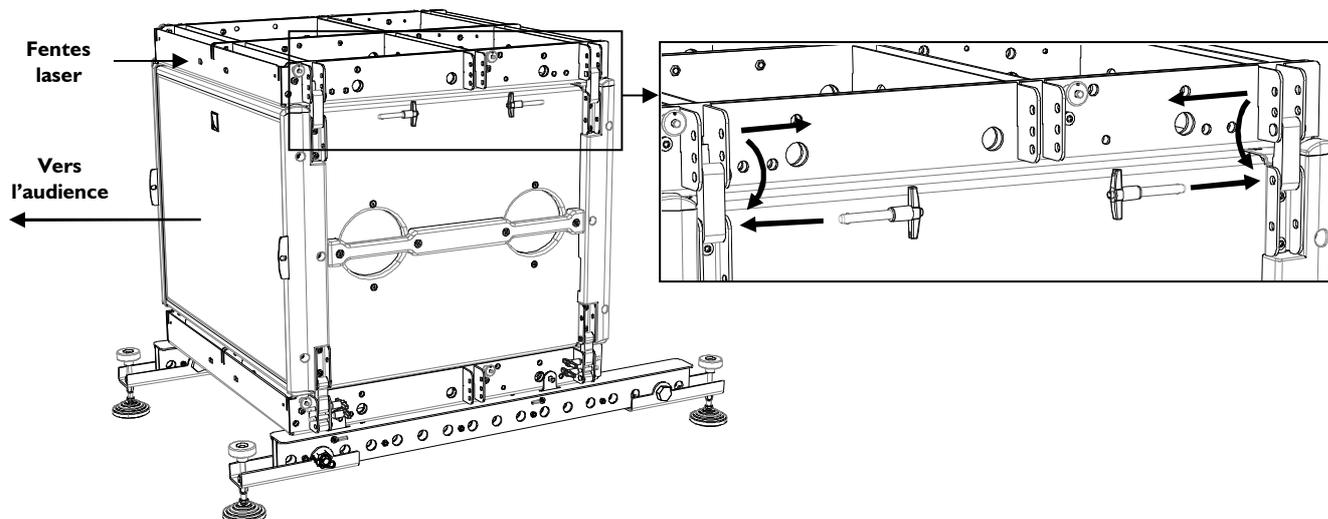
Installation d'un second M-BUMP (extension arrière pour le M-BUMP du bas de ligne)
